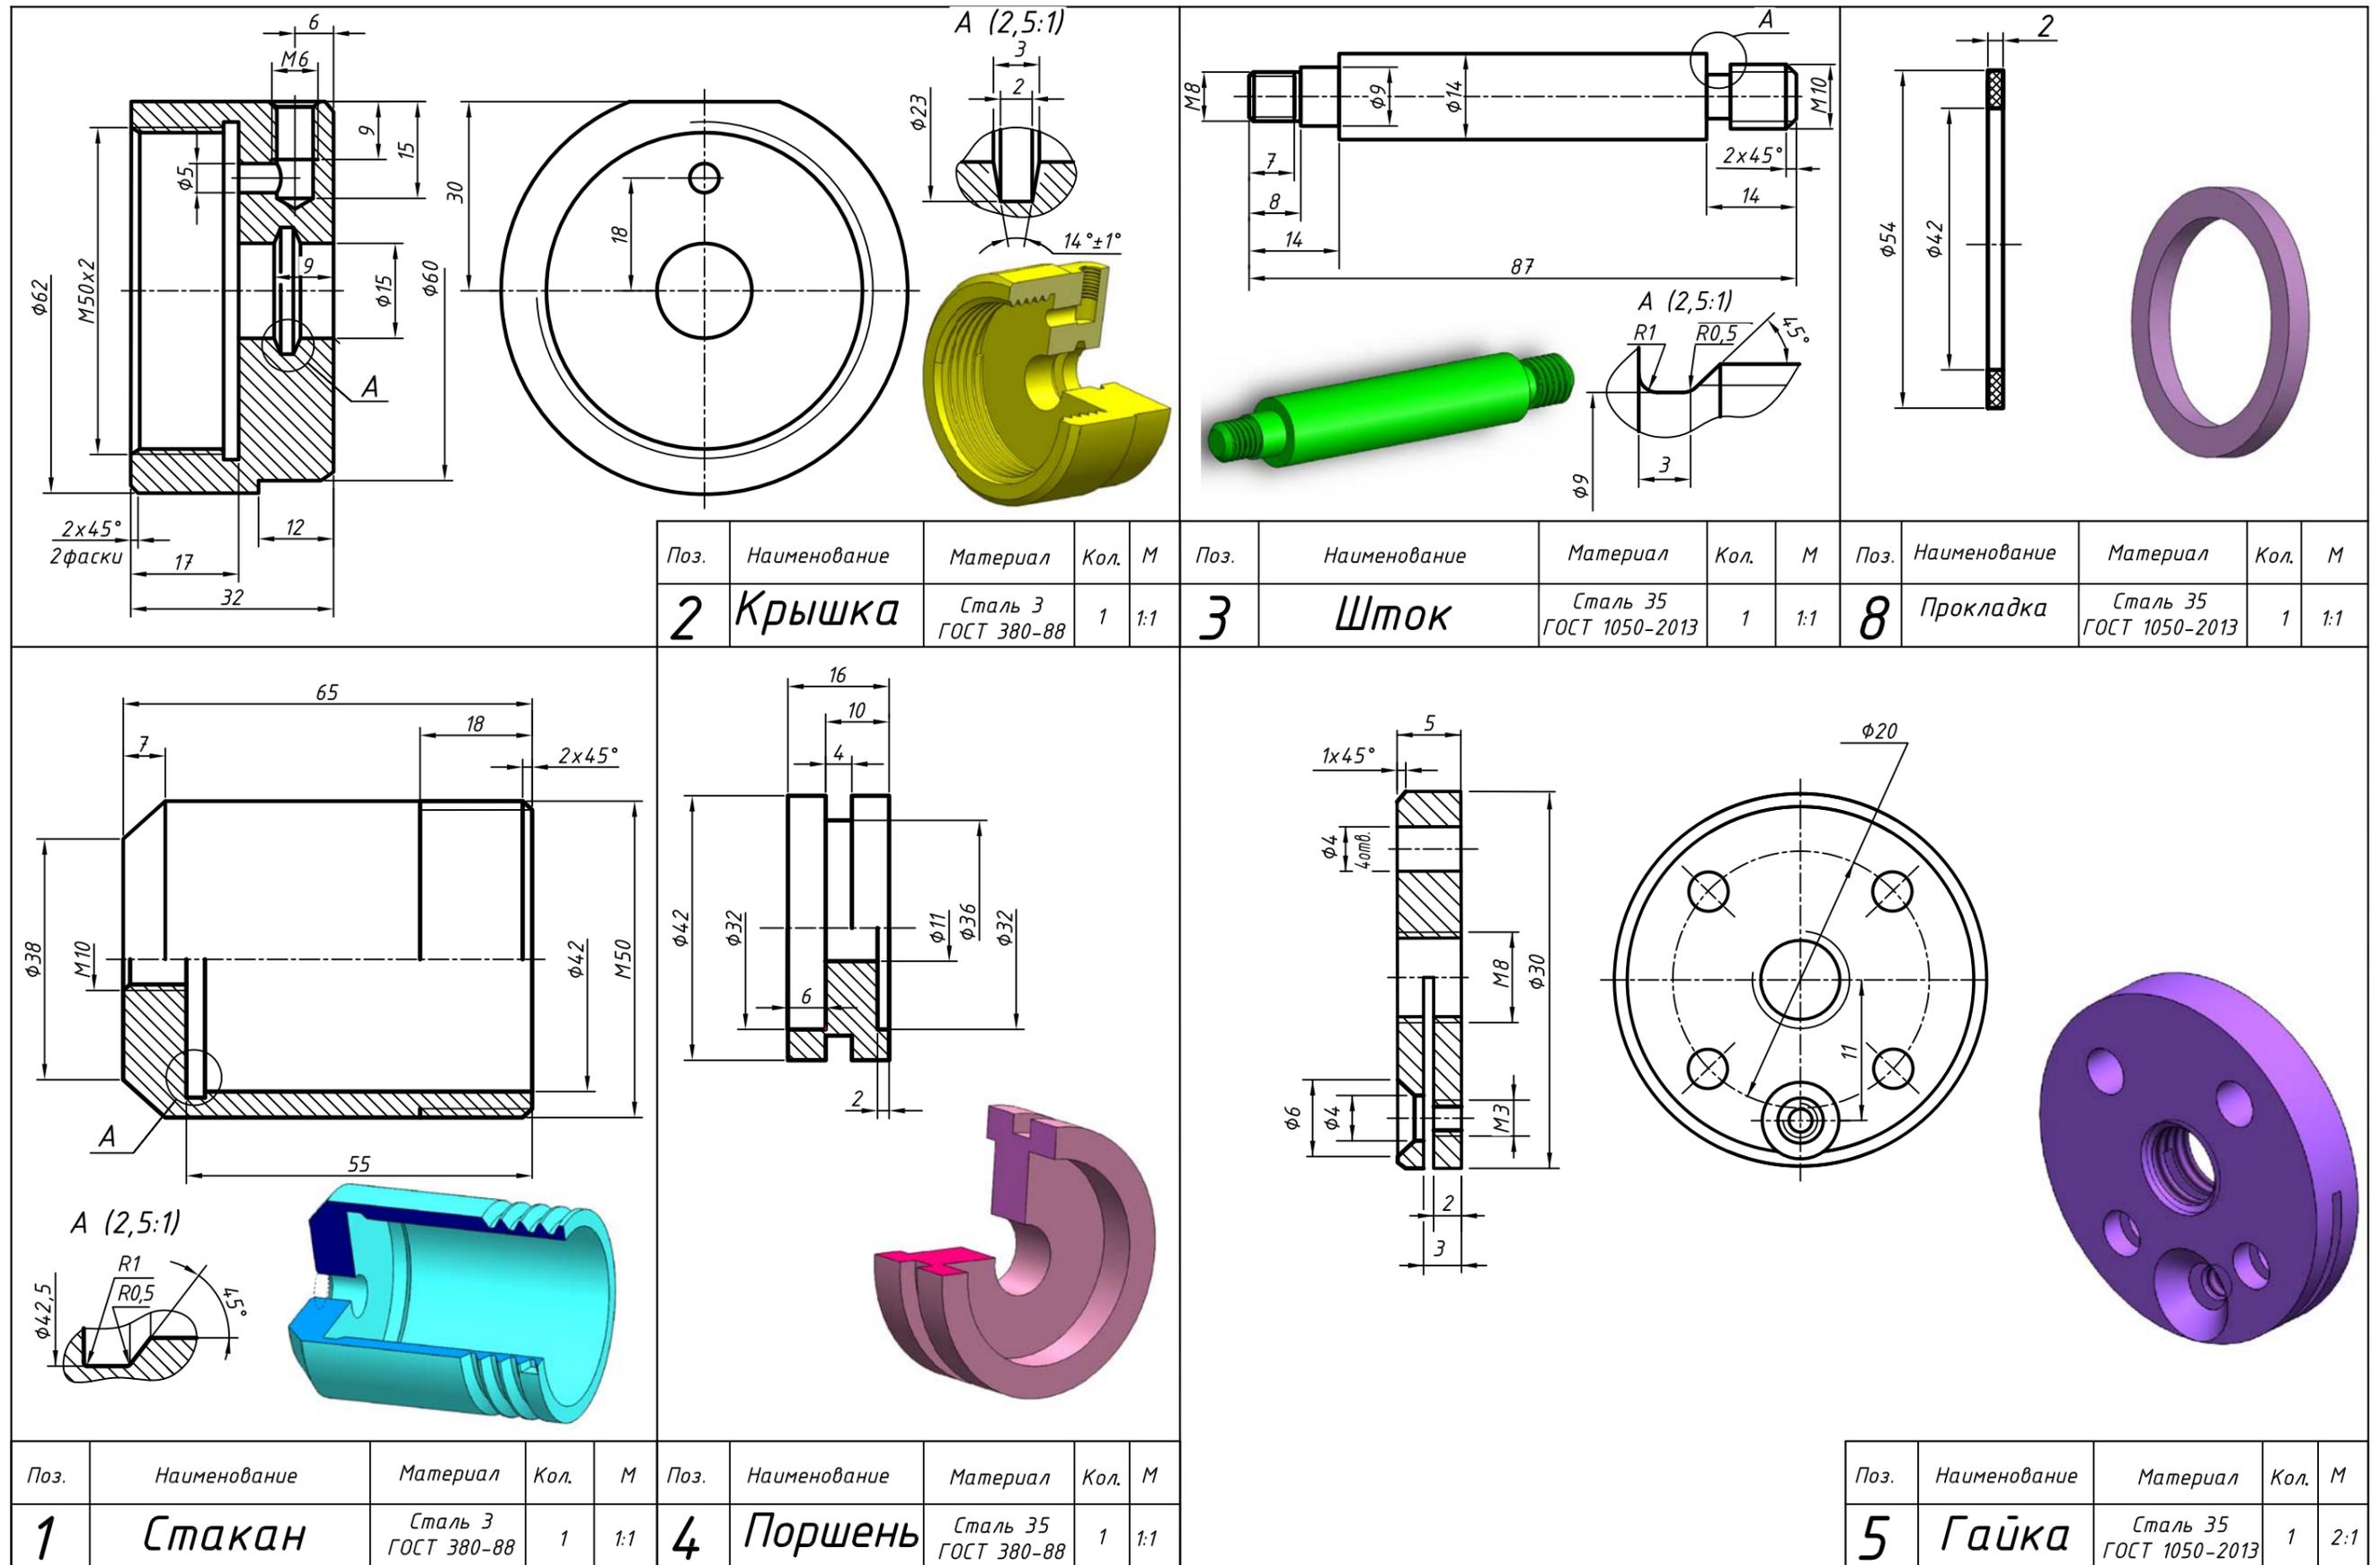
Рабочие чертежи деталей сборочного узла «Цилиндр пневматический»
